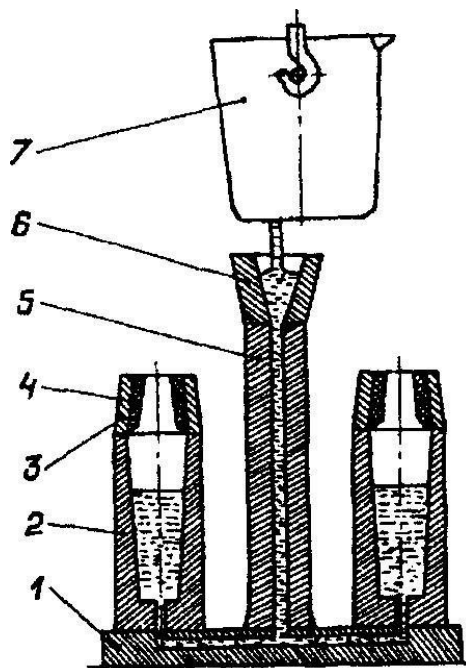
Сифонне розливання сталі: 1 - піддон; 2 - виливниця; 3 - приростова надставка; 4 — футеровка надставки; 5 - центровий ливник; 6 — чаша; 7 — ківш для розливання сталі
